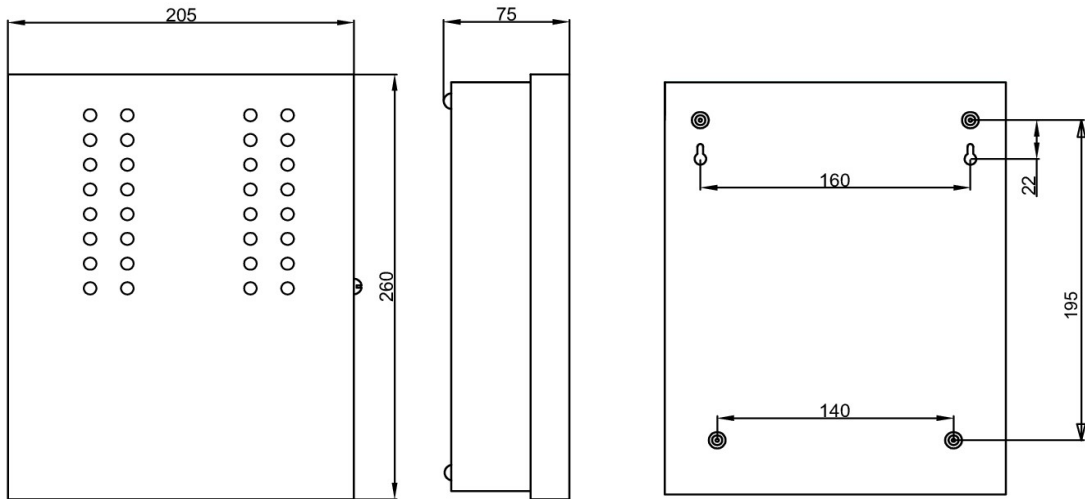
Габаритные и установочные размеры прибора, металлический корпус
